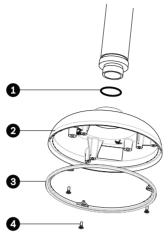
Colocação da junta circular e do anel de retenção para instalação exterior
